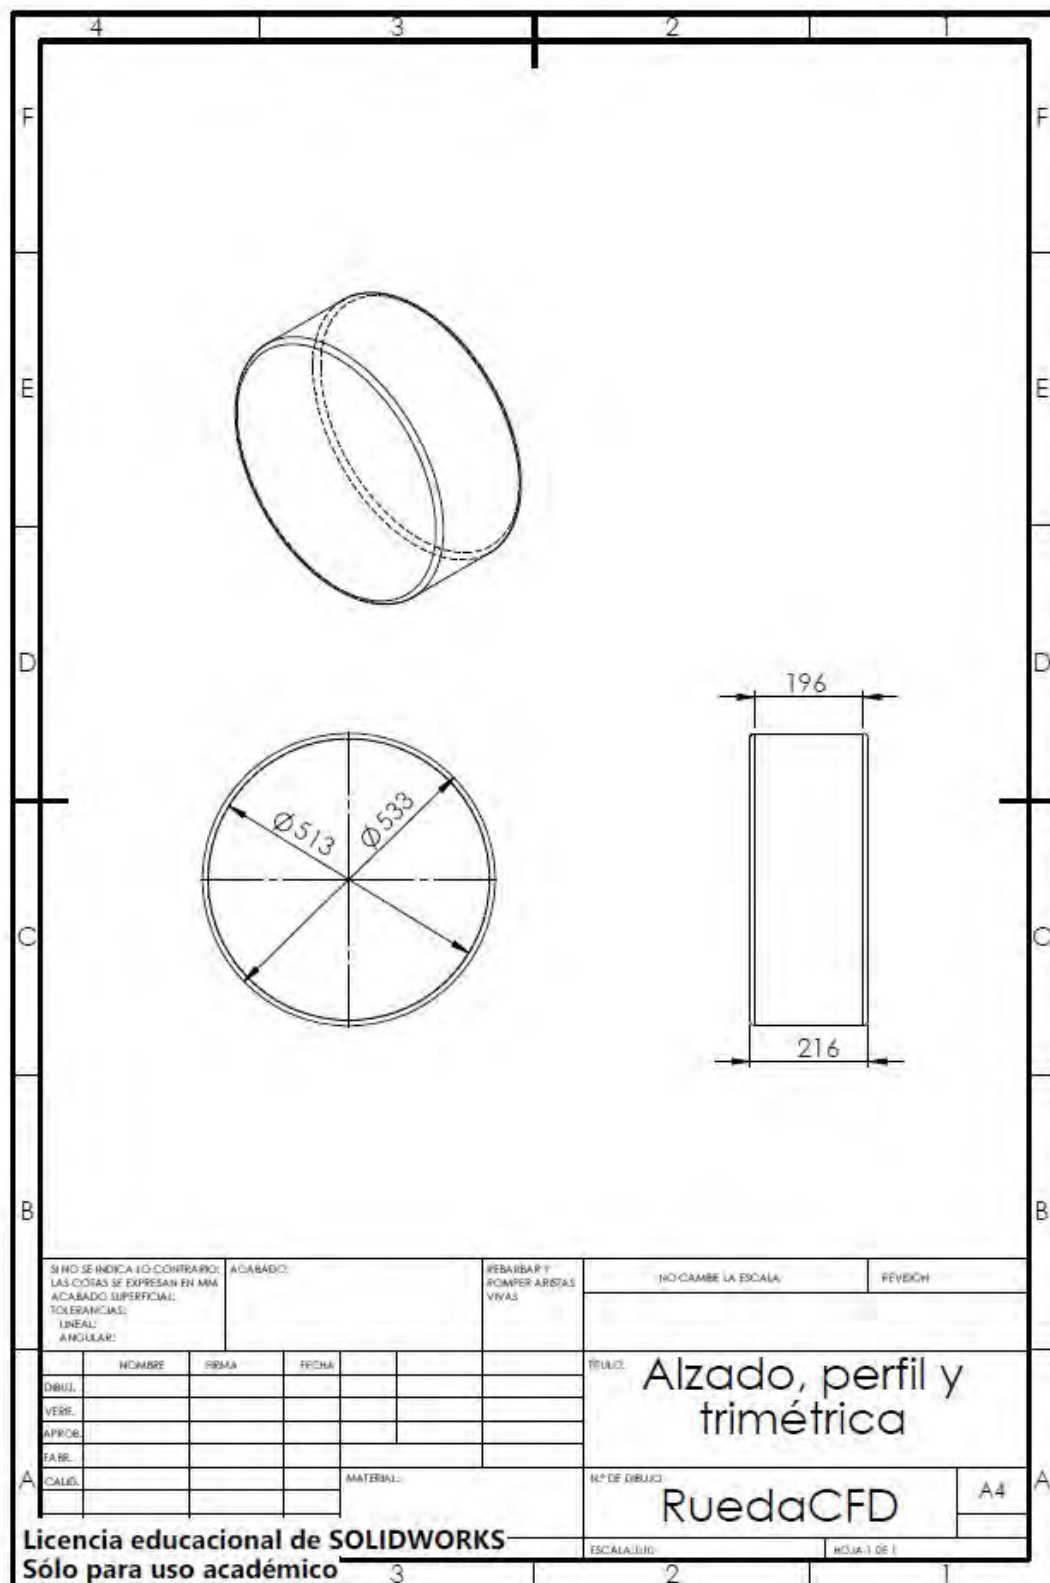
Vista de trimétrica, alzado y perfil de la rueda.
